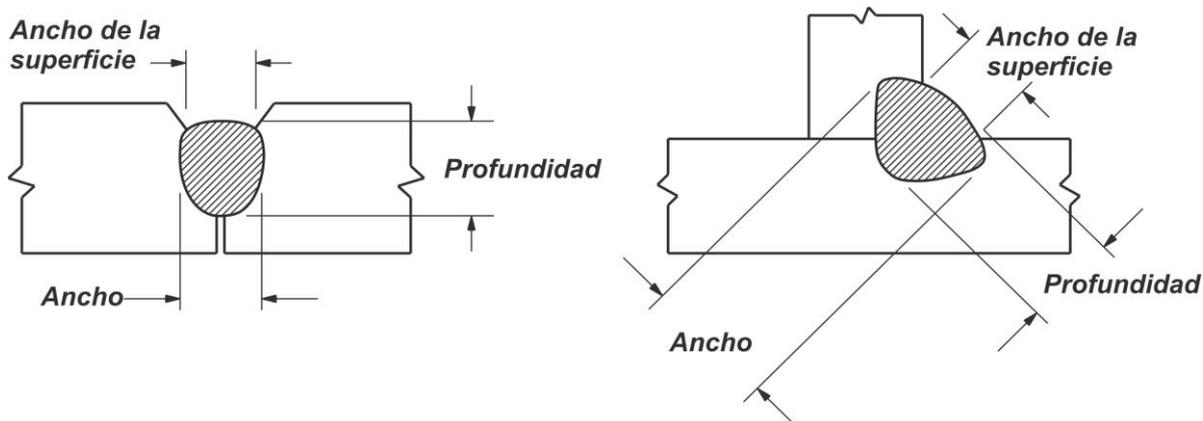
Cordón de soldadura en el cuál la profundidad y el ancho excede el ancho de la superficie o cara de la soldadura.
